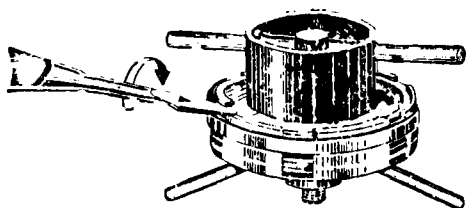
Разборка муфты сцепления при помощи приспособления.
